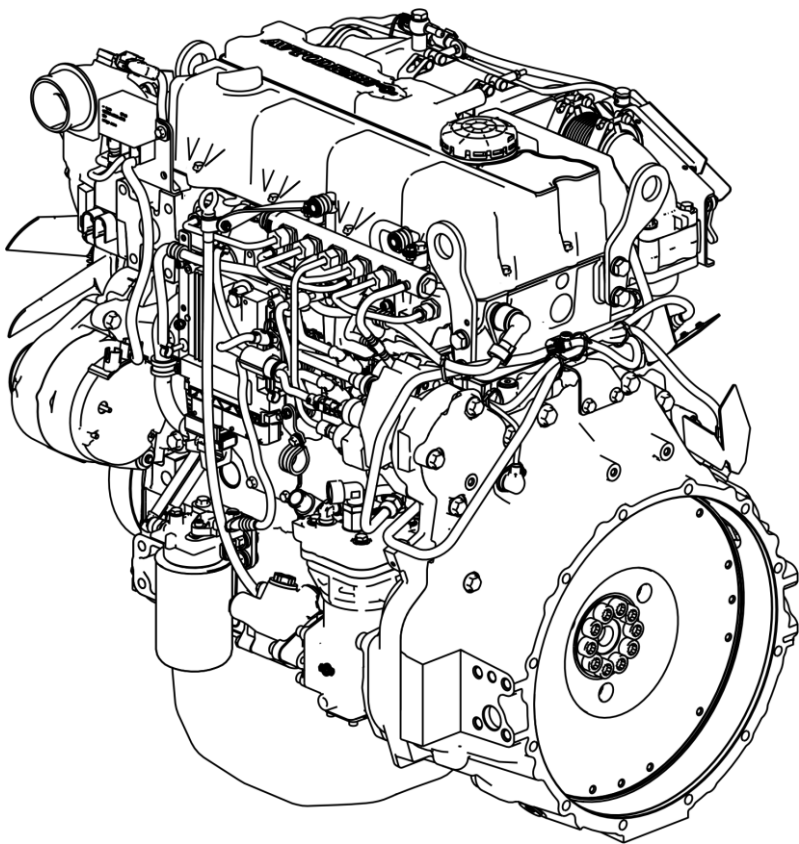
а – Двигатель ЯМЗ-53443-20 (общий вид слева)
